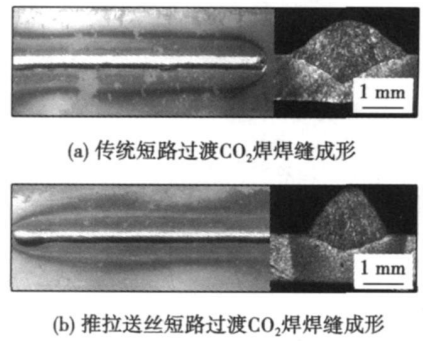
推拉送丝 CO₂ 焊与传统 CO₂ 焊焊缝形貌
